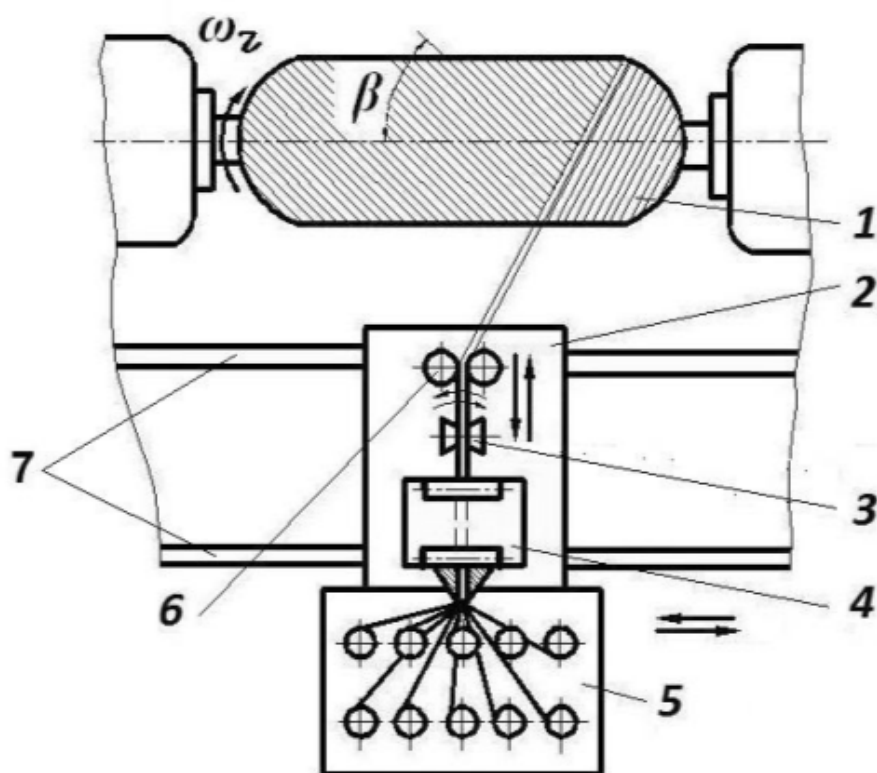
Схема формообразования изделия спиральной намоткой на станке с ЧПУ токарного типа:
